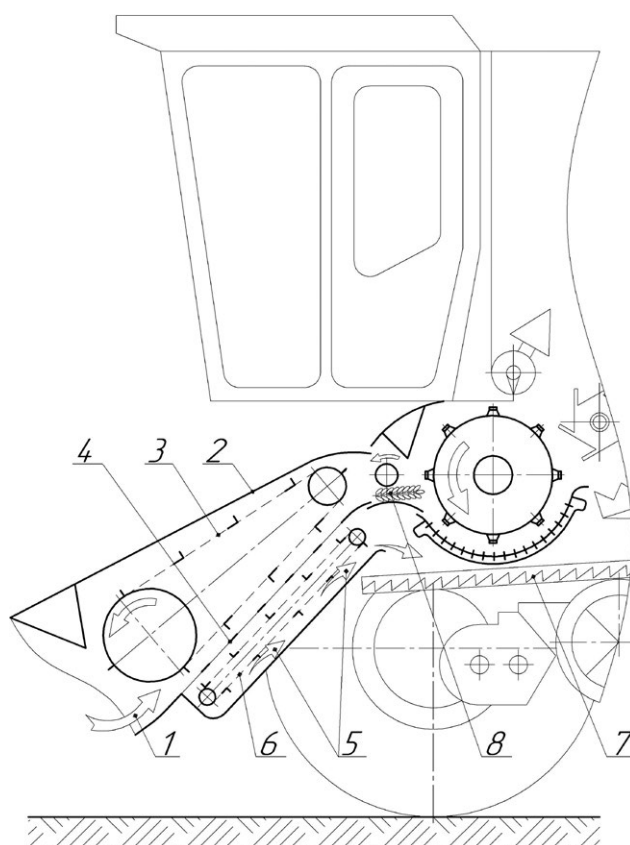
Общий вид зерноуборочного комбайна с модернизированной наклонной камерой: 1 – очесанный зерновой ворох; 2 – наклонная камера; 3 – плавающий транспортер; 4 – решетчатое днище; 5 – свободное зерно; 6 – устройство для отвода свободного зерна; 7 – транспортная доска; 8 – оставшаяся часть первичного вороха.
